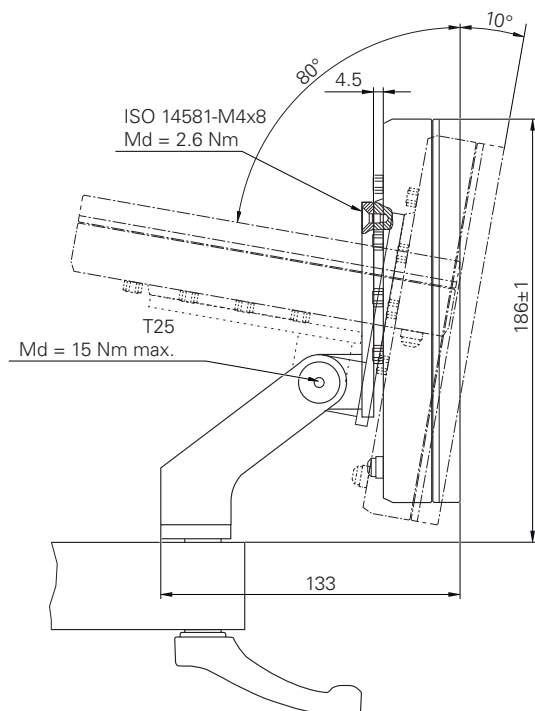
Dimensiones del aparato con soporte Multi-Pos
